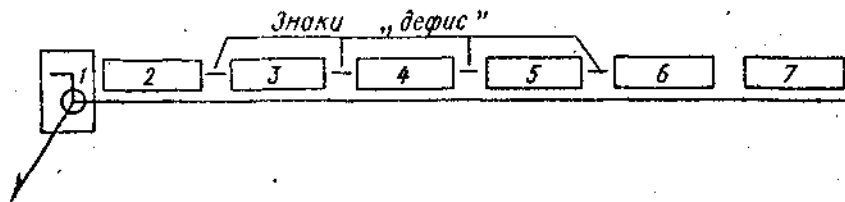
Структура условного обозначения шва сварного соединения:
